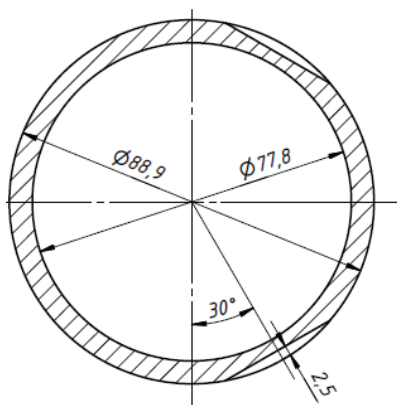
Опытный образец трубы КСМ типоразмера НQ
